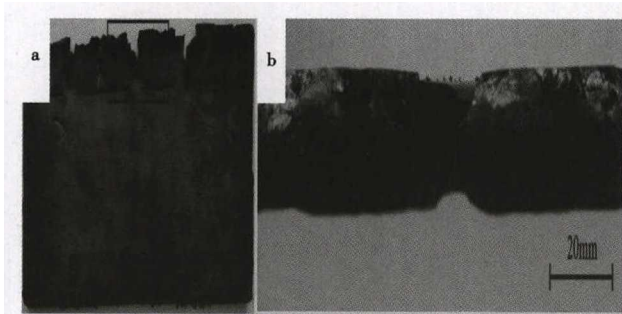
(a) 304L 开裂热轧板表面形貌 (b) 304L 开裂热轧板截面形貌
